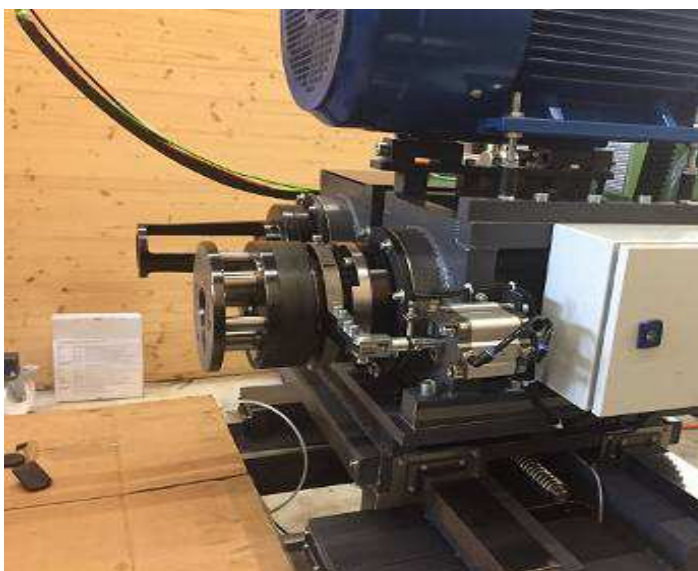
Der Rollierkopf der alten Maschine geht jetzt auch auf der neuen WIAP CNC Maschine Öffnen und schliessen über den Zylinder. Der Längendehnfaktor des Werkstückes durch das Rollieren wird mit einem R Parameter im CNC Programm automatisch berechnet und berücksichtigt
